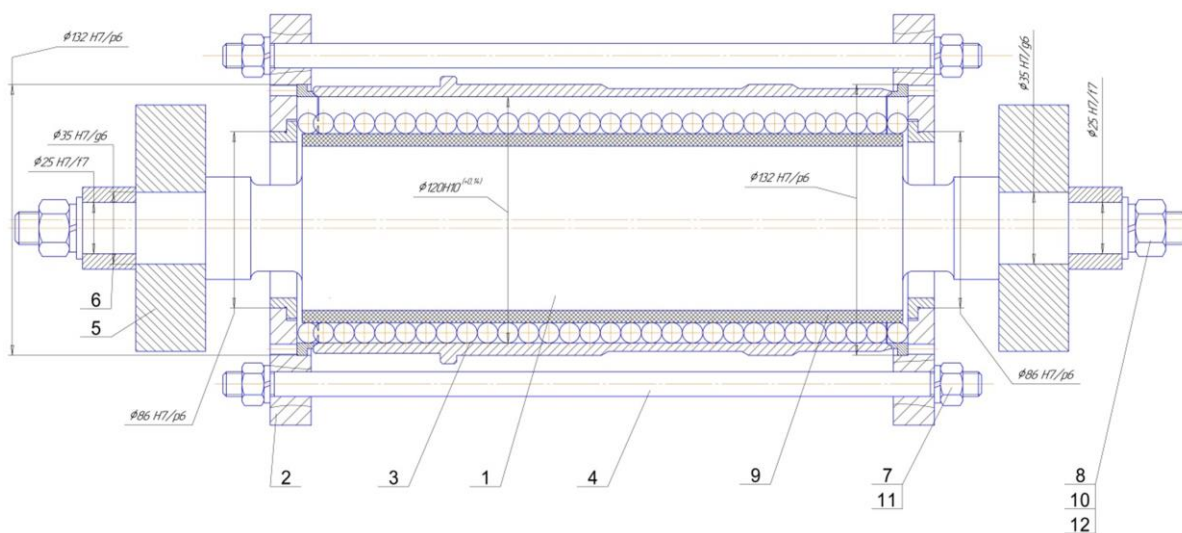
Принципова схема технологічної системи фінішної обробки поверхневим пластичним деформуванням технологічне середовище, що її реалізує
